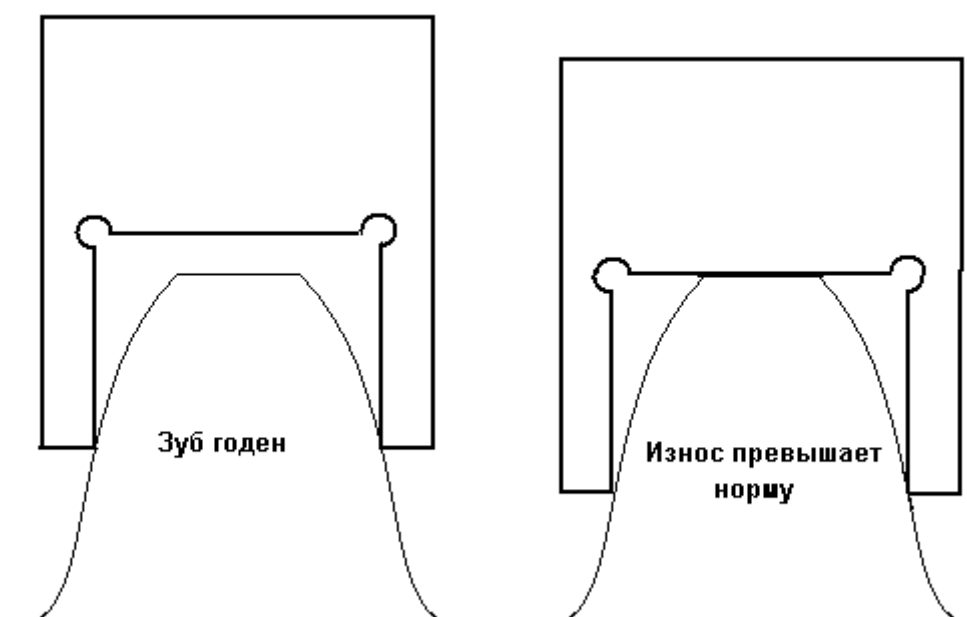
Шаблон для выбраковки зубьев шестерни по толщине
